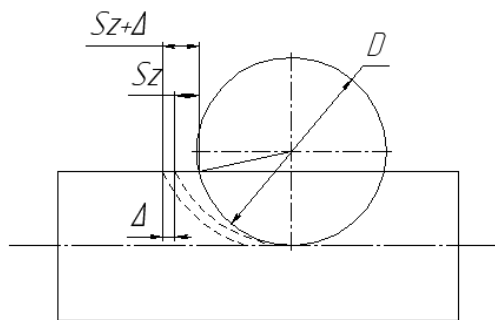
Схема несимметричного торцового фрезерования
